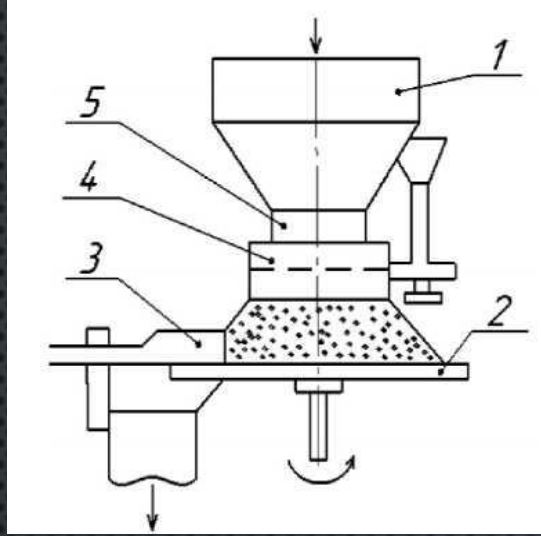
Тарілчастий дозатор: 1 – бункер; 2 – тарілка; 3 – скребок; 4 і 5 – рухомий і нерухомий патрубки
